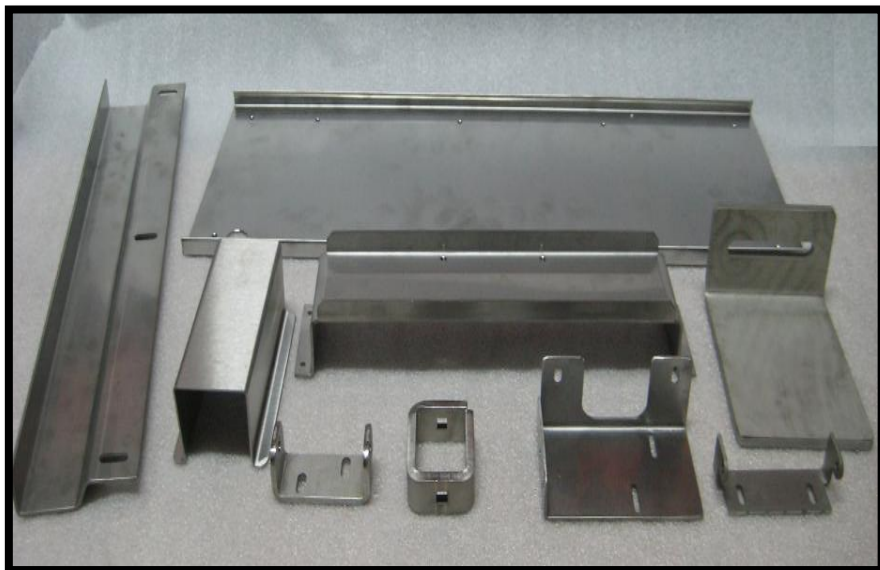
Peças cortadas e quinadas na secção de corte e quinagem
